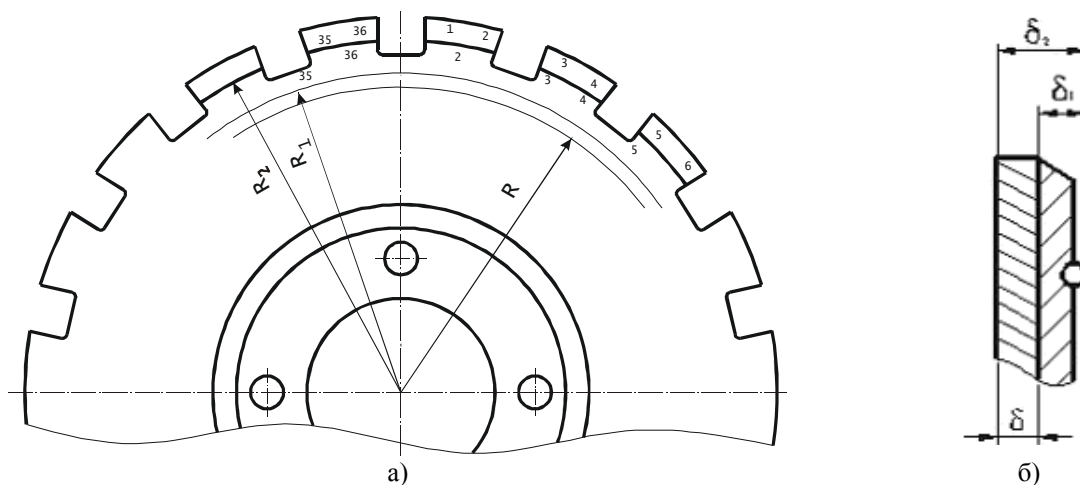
а – ніж-гичкоріз, підготовлений для вимірювання товщини шару наплавлюваного металу і прогинів; б – переріз в зоні наплавлення
